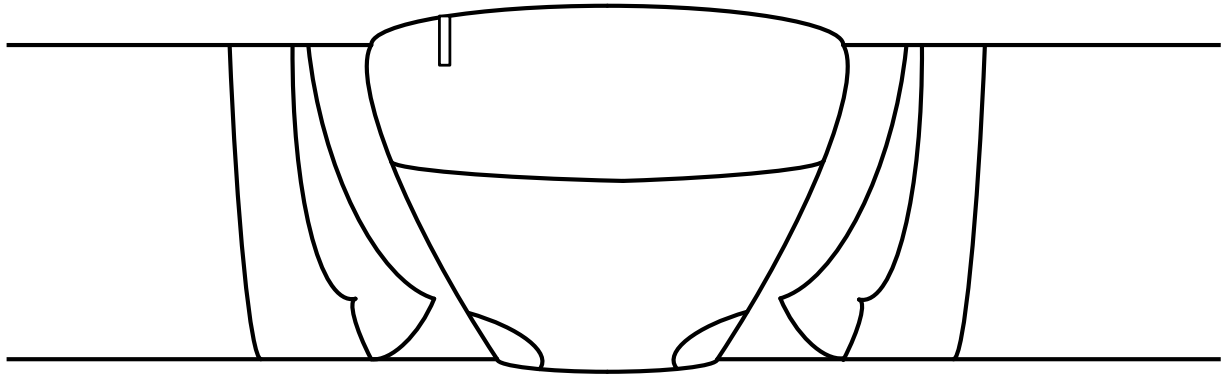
Расчетная схема с трещиноподобным дефектом в сварном шве и основном металле
